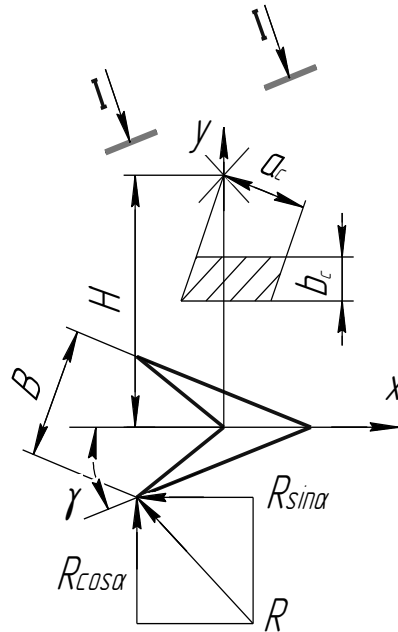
Розрахункова схема стійки лапи культиватора
